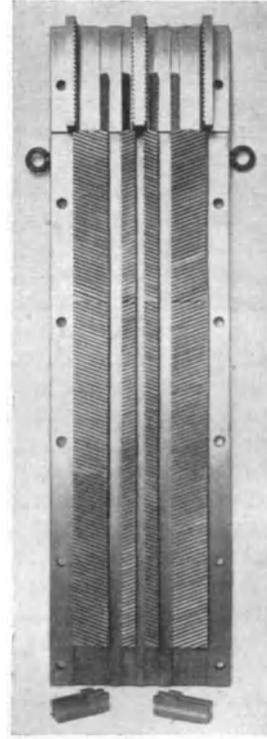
Gebautes Räumzeug für Senkrecht-Außenräummaschinen (Schilling).
